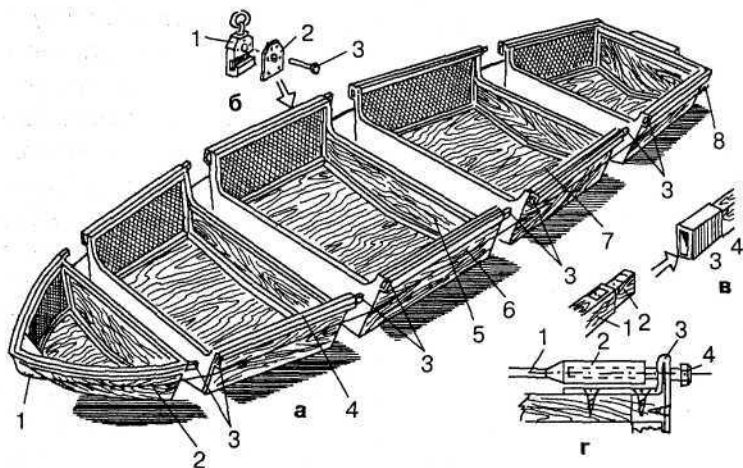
Общий вид и детали конструкции: а — корпус (в разложенном виде): 1 — стяжной трос, 2 — носовая секция, 3 — стыковые узлы наружного привального бруса, 4 — внутренний привальный брус, 5 — торцевая перегородка (диафрагма), 6 — обшивка борта (фанера толщиной 3 мм), 7 — обшивка дна (фанера толщиной 4 мм), 8 — натяжное устройство; б — крепление уключины: 1 — подуключник, 2 — накладка, 3 — стяжной болт; в — конструкции стыкового узла наружного привального бруса: 1 — привальный брус, 2 — шип, 3 — гнездо (кровельное железо), 4 — привальный брус следующей секции; г — устройство для натяжки троса: 1 — трос, 2 — резьбовая втулка, 3 — кронштейн, 4 — натяжной болт
